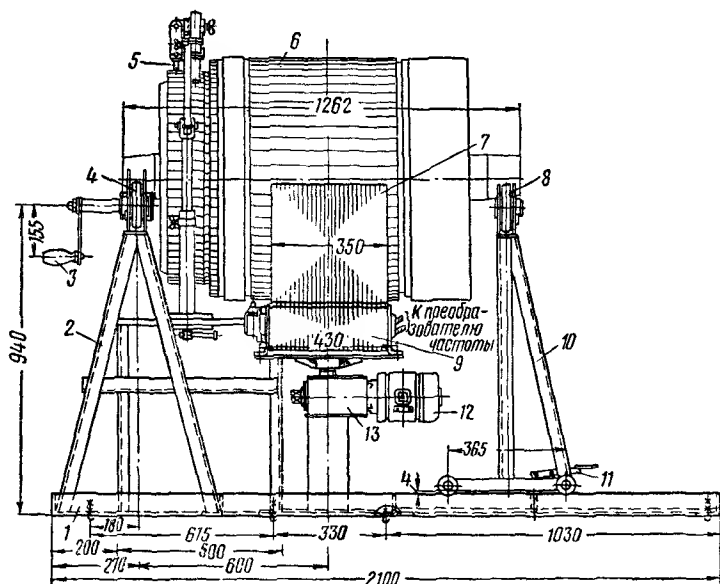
Стенд для проверки витковой изоляции обмоток якорей тяговых двигателей:
